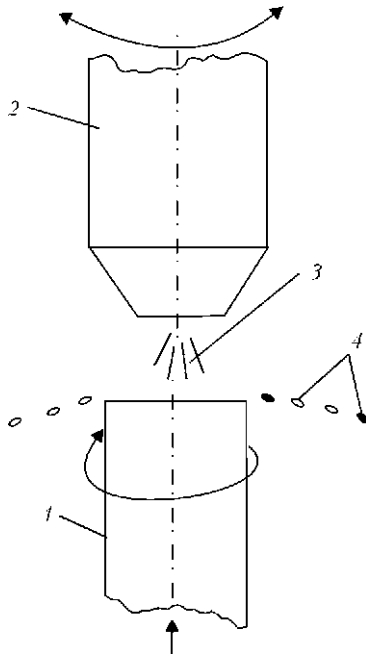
Схема термоцентробежного распыления: 1 – заготовка (расходуемый стержень); 2 – плазматрон; 3 – плазменная дуга; 4 – капли жидкого металла
